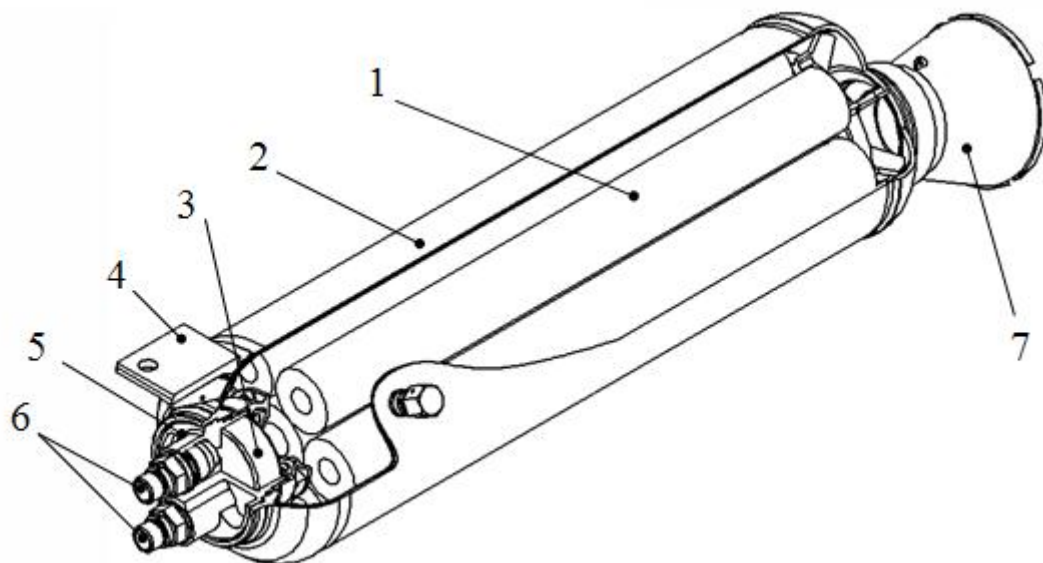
Устройство твердотопливного порохового ракетного двигателя
